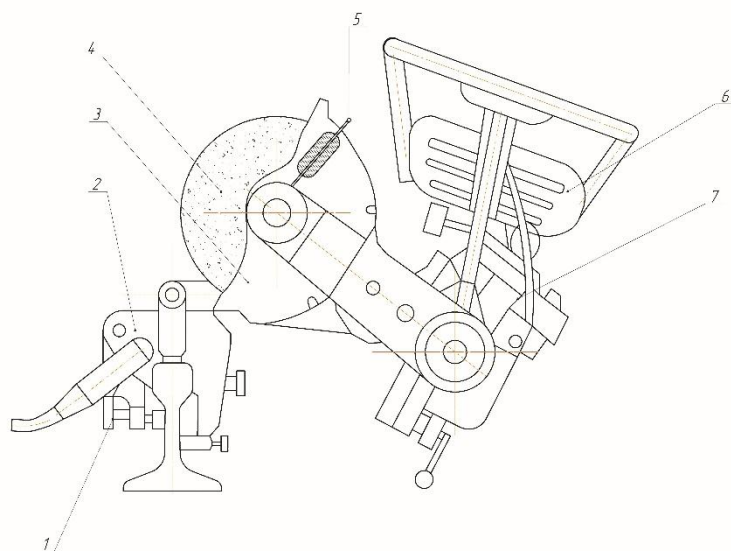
Общий вид рельсорезного станка РМК: 1 – винт для крепления захвата на рельсе; 2 – эксцентриковый захват; 3 – защитный кожух; 4 – режущий абразивный диск; 5 – фиксатор положения кожуха; 6 – бензобак; 7 – двигатель
